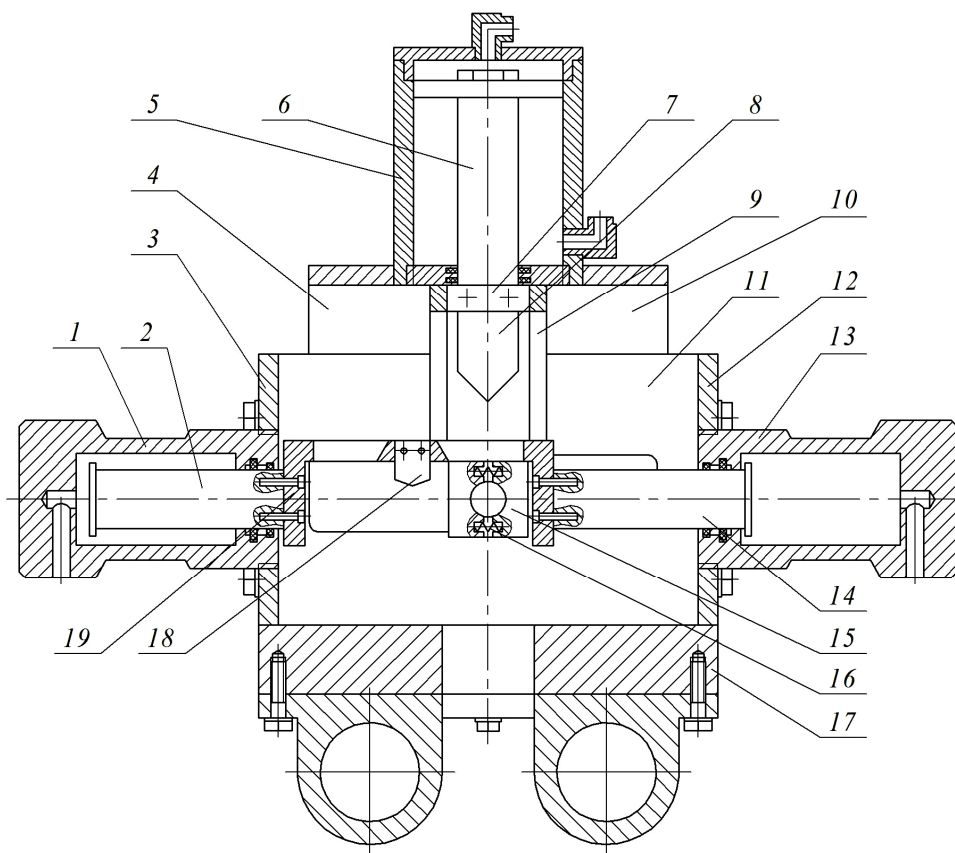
Конструктивная схема режущего блока летучих ножниц трубосварочного стана
